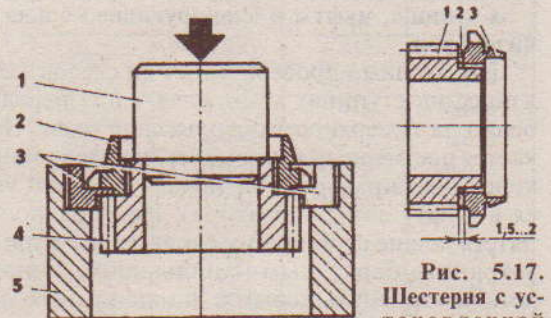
Выпрессовка зубчатого венца: 1 - упор; 2 - зубчатый венец; 3 - полукольца; 4 - шестерня; 5 - подставка
